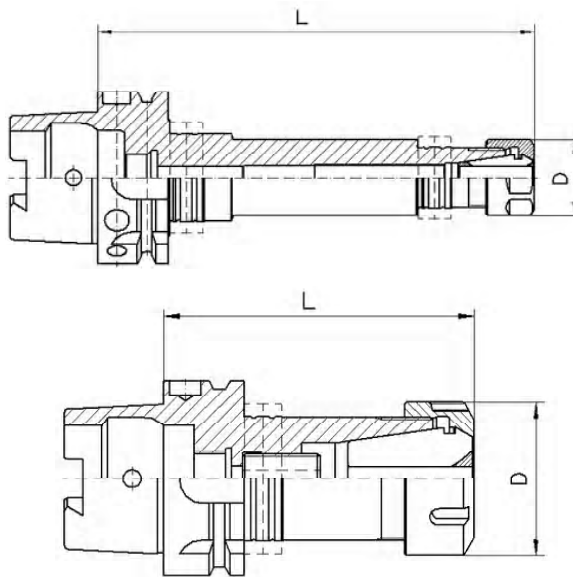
Цанговые патроны HSK-63A для крепления свёрл
